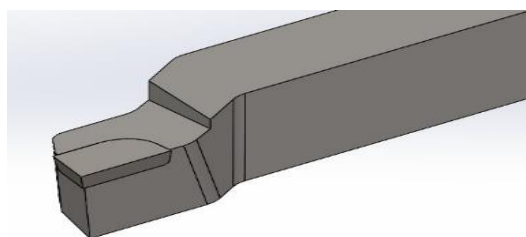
Токарный подрезной резец с пластиной из быстрорежущей стали P18
